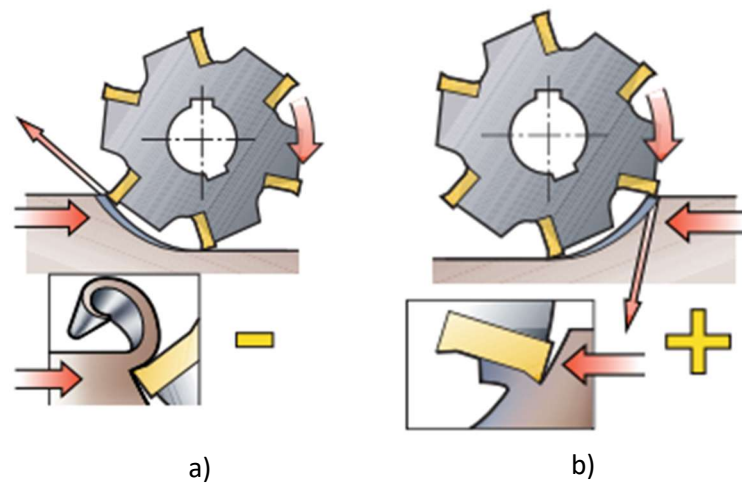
Movimento discordante (a), movimento concordante (b) [6].
